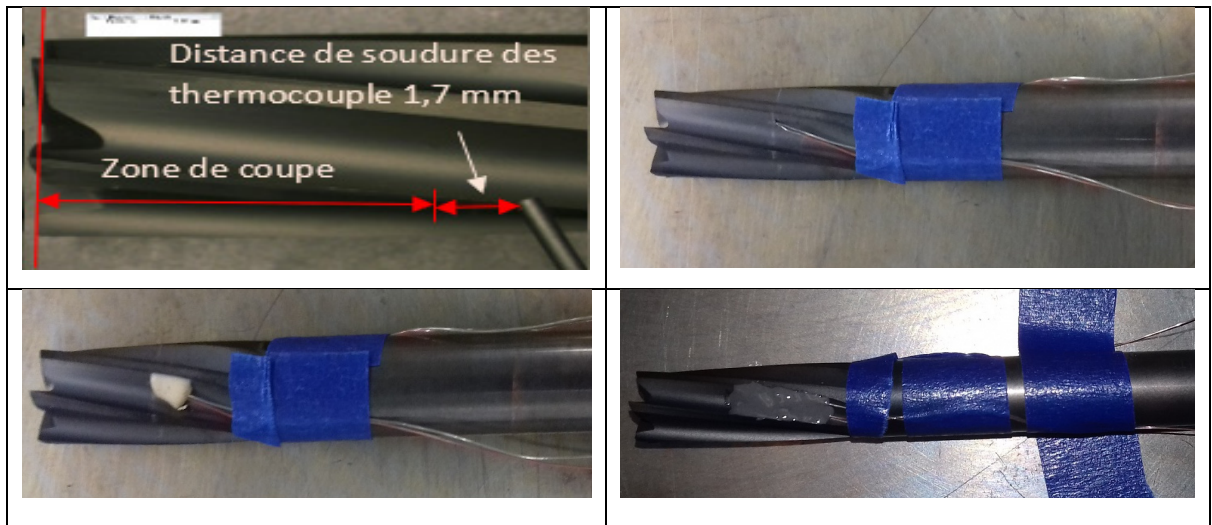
Soudure des thermocouples sur l'outil de coupe
